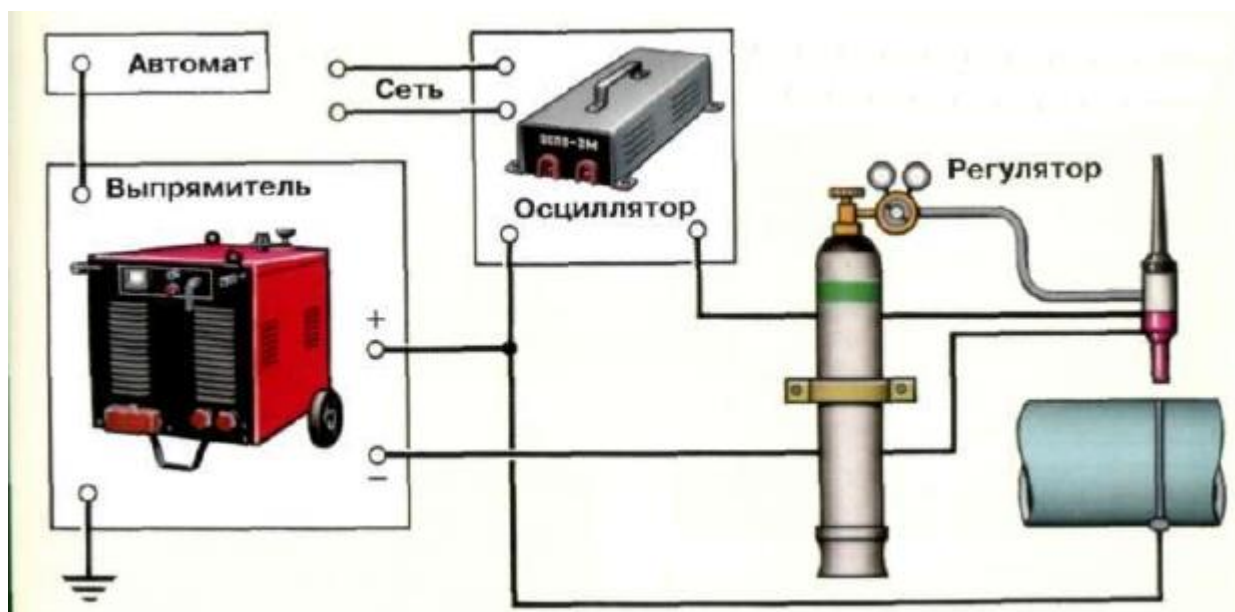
Сварка неплавящимся электродом в защитном газе
